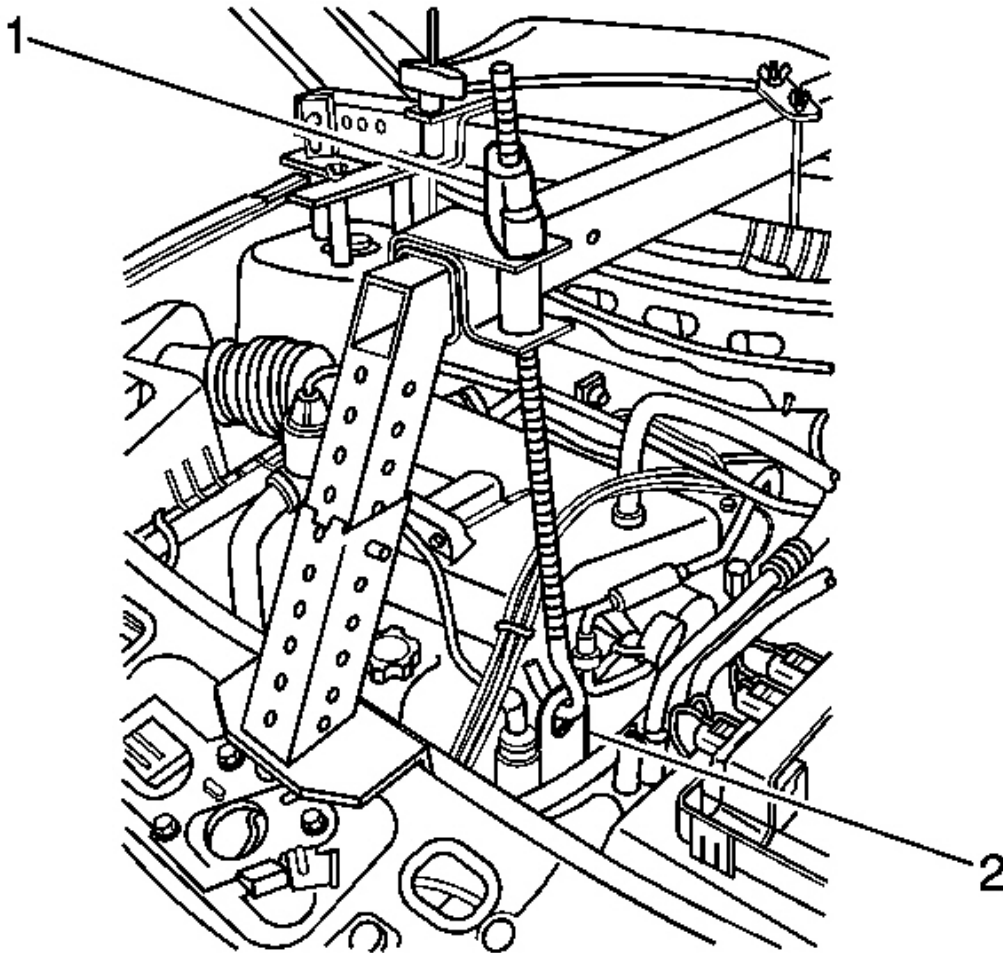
Vista de la elevación Cortesía conjunto del gancho de General Motors Corp.
